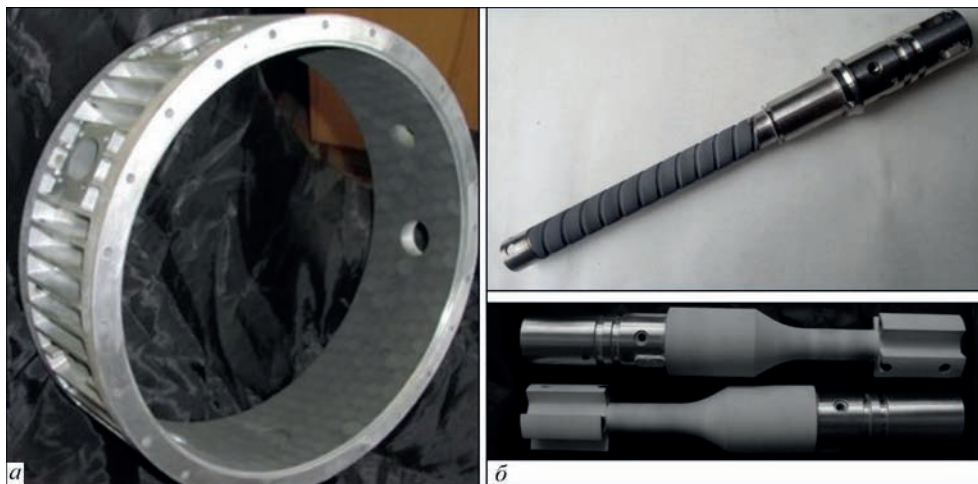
Деталі з легких сплавів: *а* – корпус роторно-поршневого двигуна; *б* – деталі бурової телеметрії
